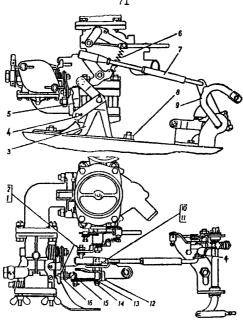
Установка привода акселератора пвигателя ГАЗ-53-07
